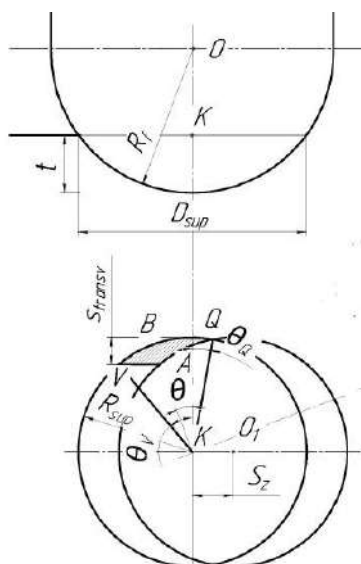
Схема расчета угла контакта зуба фрезы
